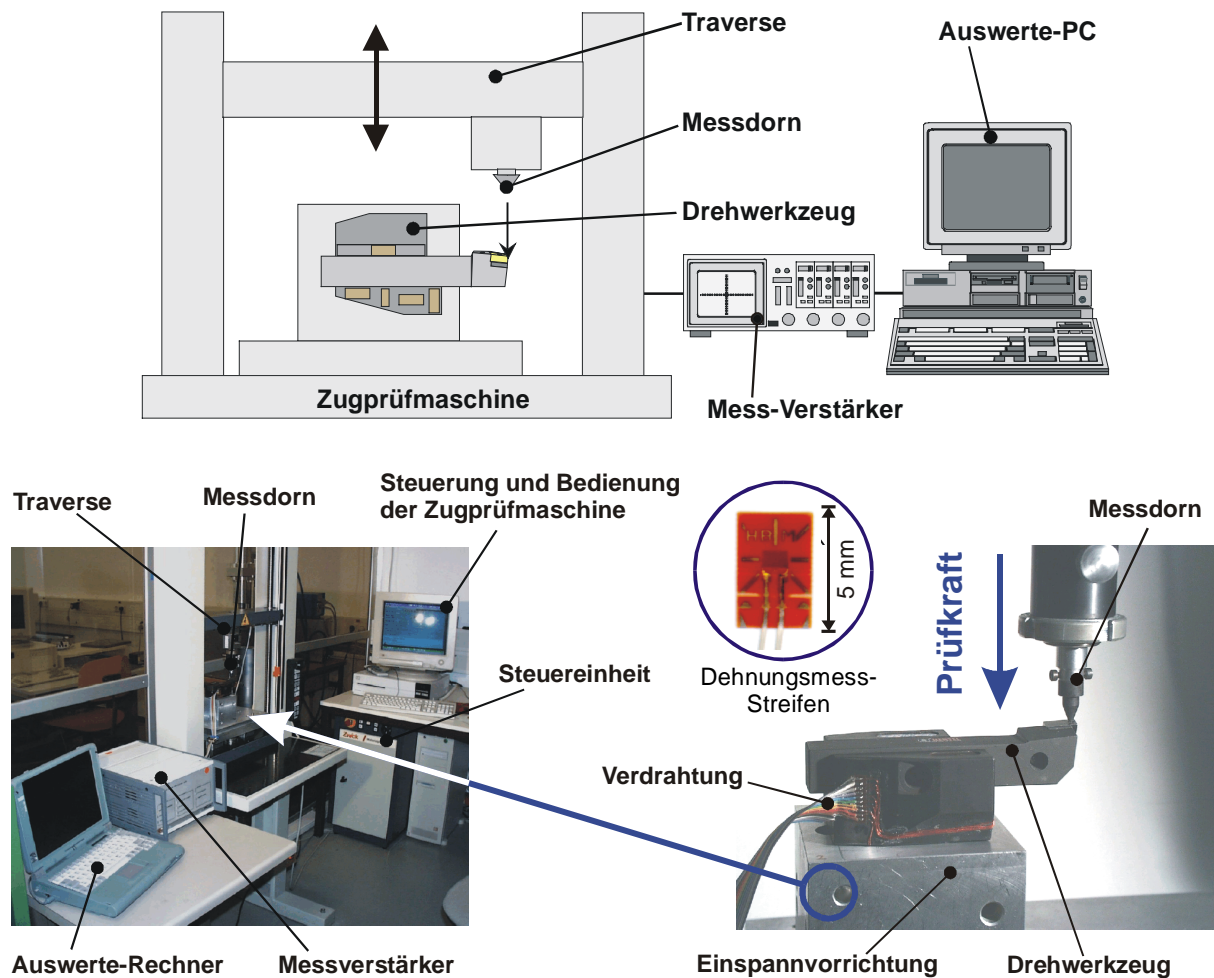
Belastung des Drehmeißel in der Zugprüfmaschine mit definierter Kraft
